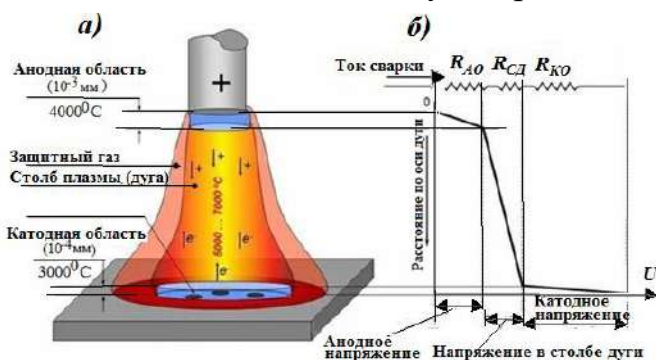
Строение и свойства сварочной дуги
